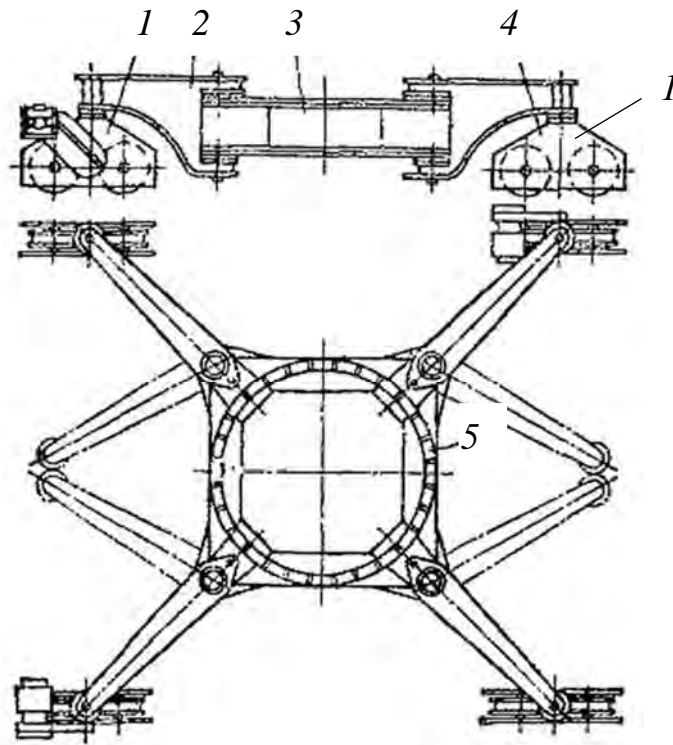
Опорная рама тяжелого крана: 1 – неприводные ходовые тележки; 2 – кронштейн; 3 – опорная конструкция; 4 – приводная тележка; 5 – место установки поворотного круга
